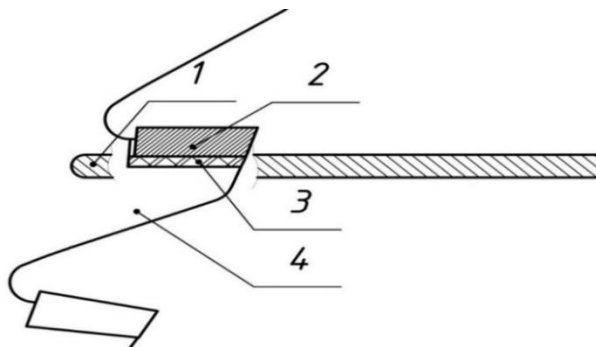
Расположение рабочей части индуктора относительно спаиваемых деталей. 1 – индуктор, 2 – наплавляемая твердосплавная пластина, 3 – припой, 4 – корпус индуктора.
